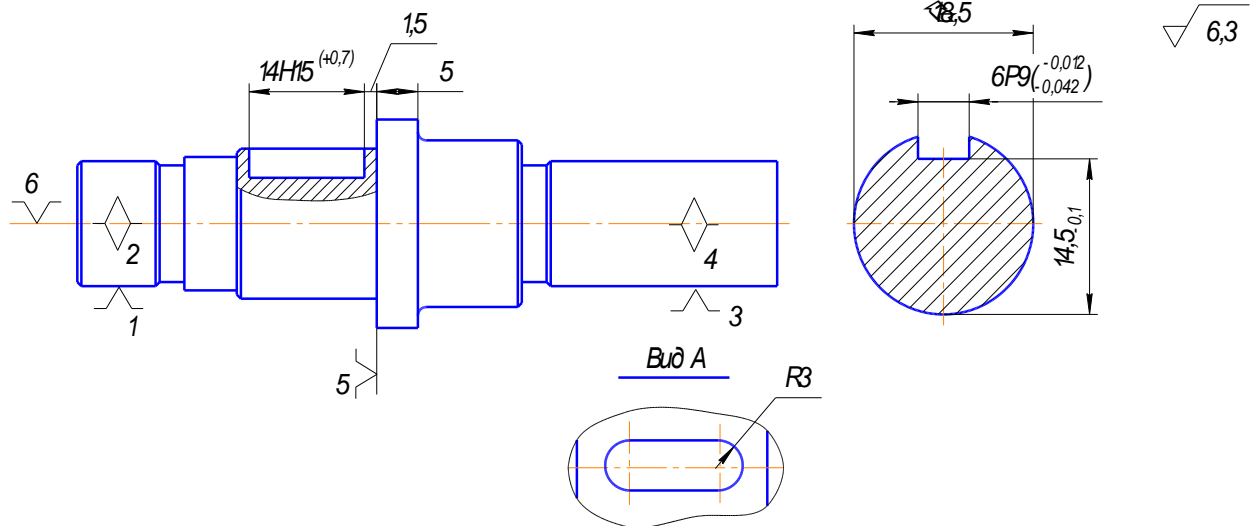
Ескіз на фрезерування паза $25P9_{-0,074}^{-0,022}$ валу 1106.03.05.092А
